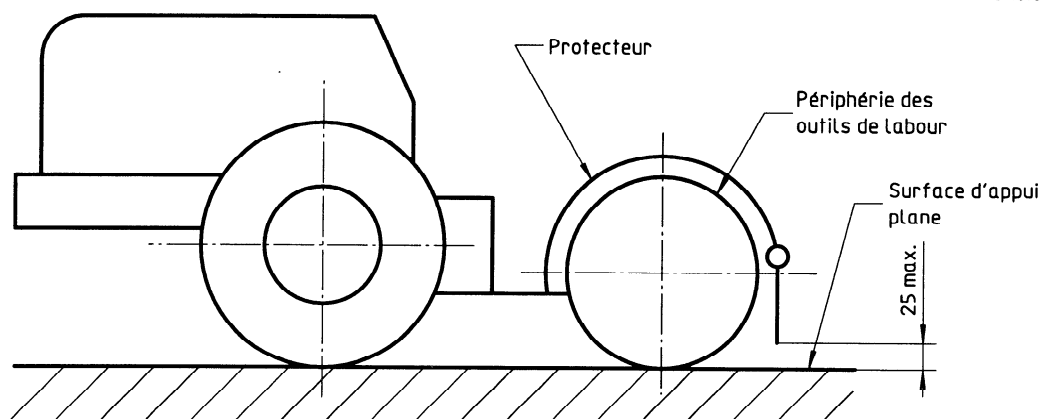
Dispositifs de protection des outils de labour — Motoculteurs à fraise arrière
